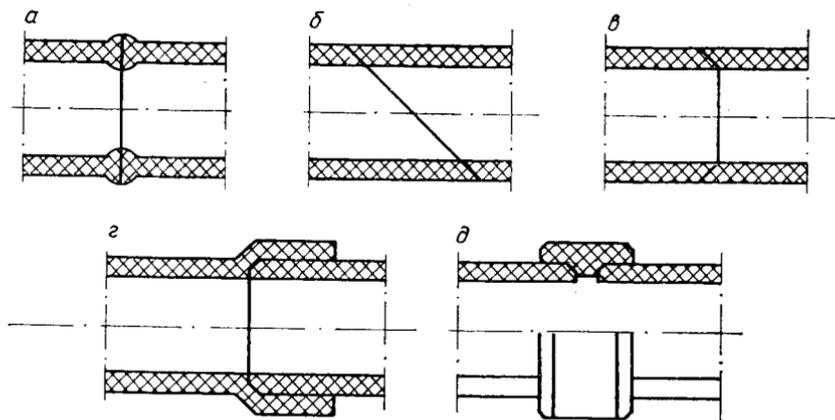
Конструкции сварных соединений труб из термопластов: а — встык; б — в «кус»; в — в конус; г — в раструб; д — с накладной муфтой.
